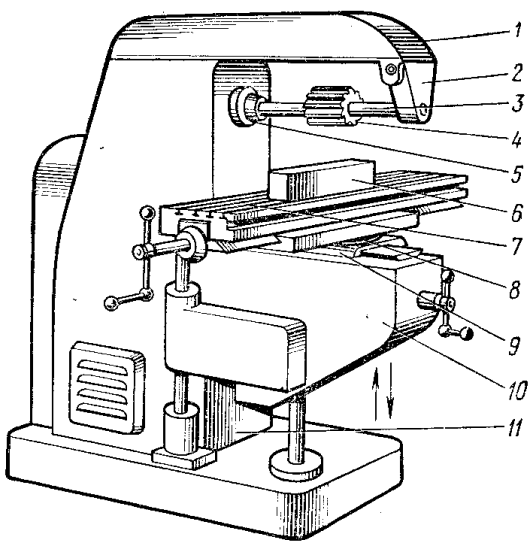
Зовнішній вигляд горизонтально-фрезерного верстату :
